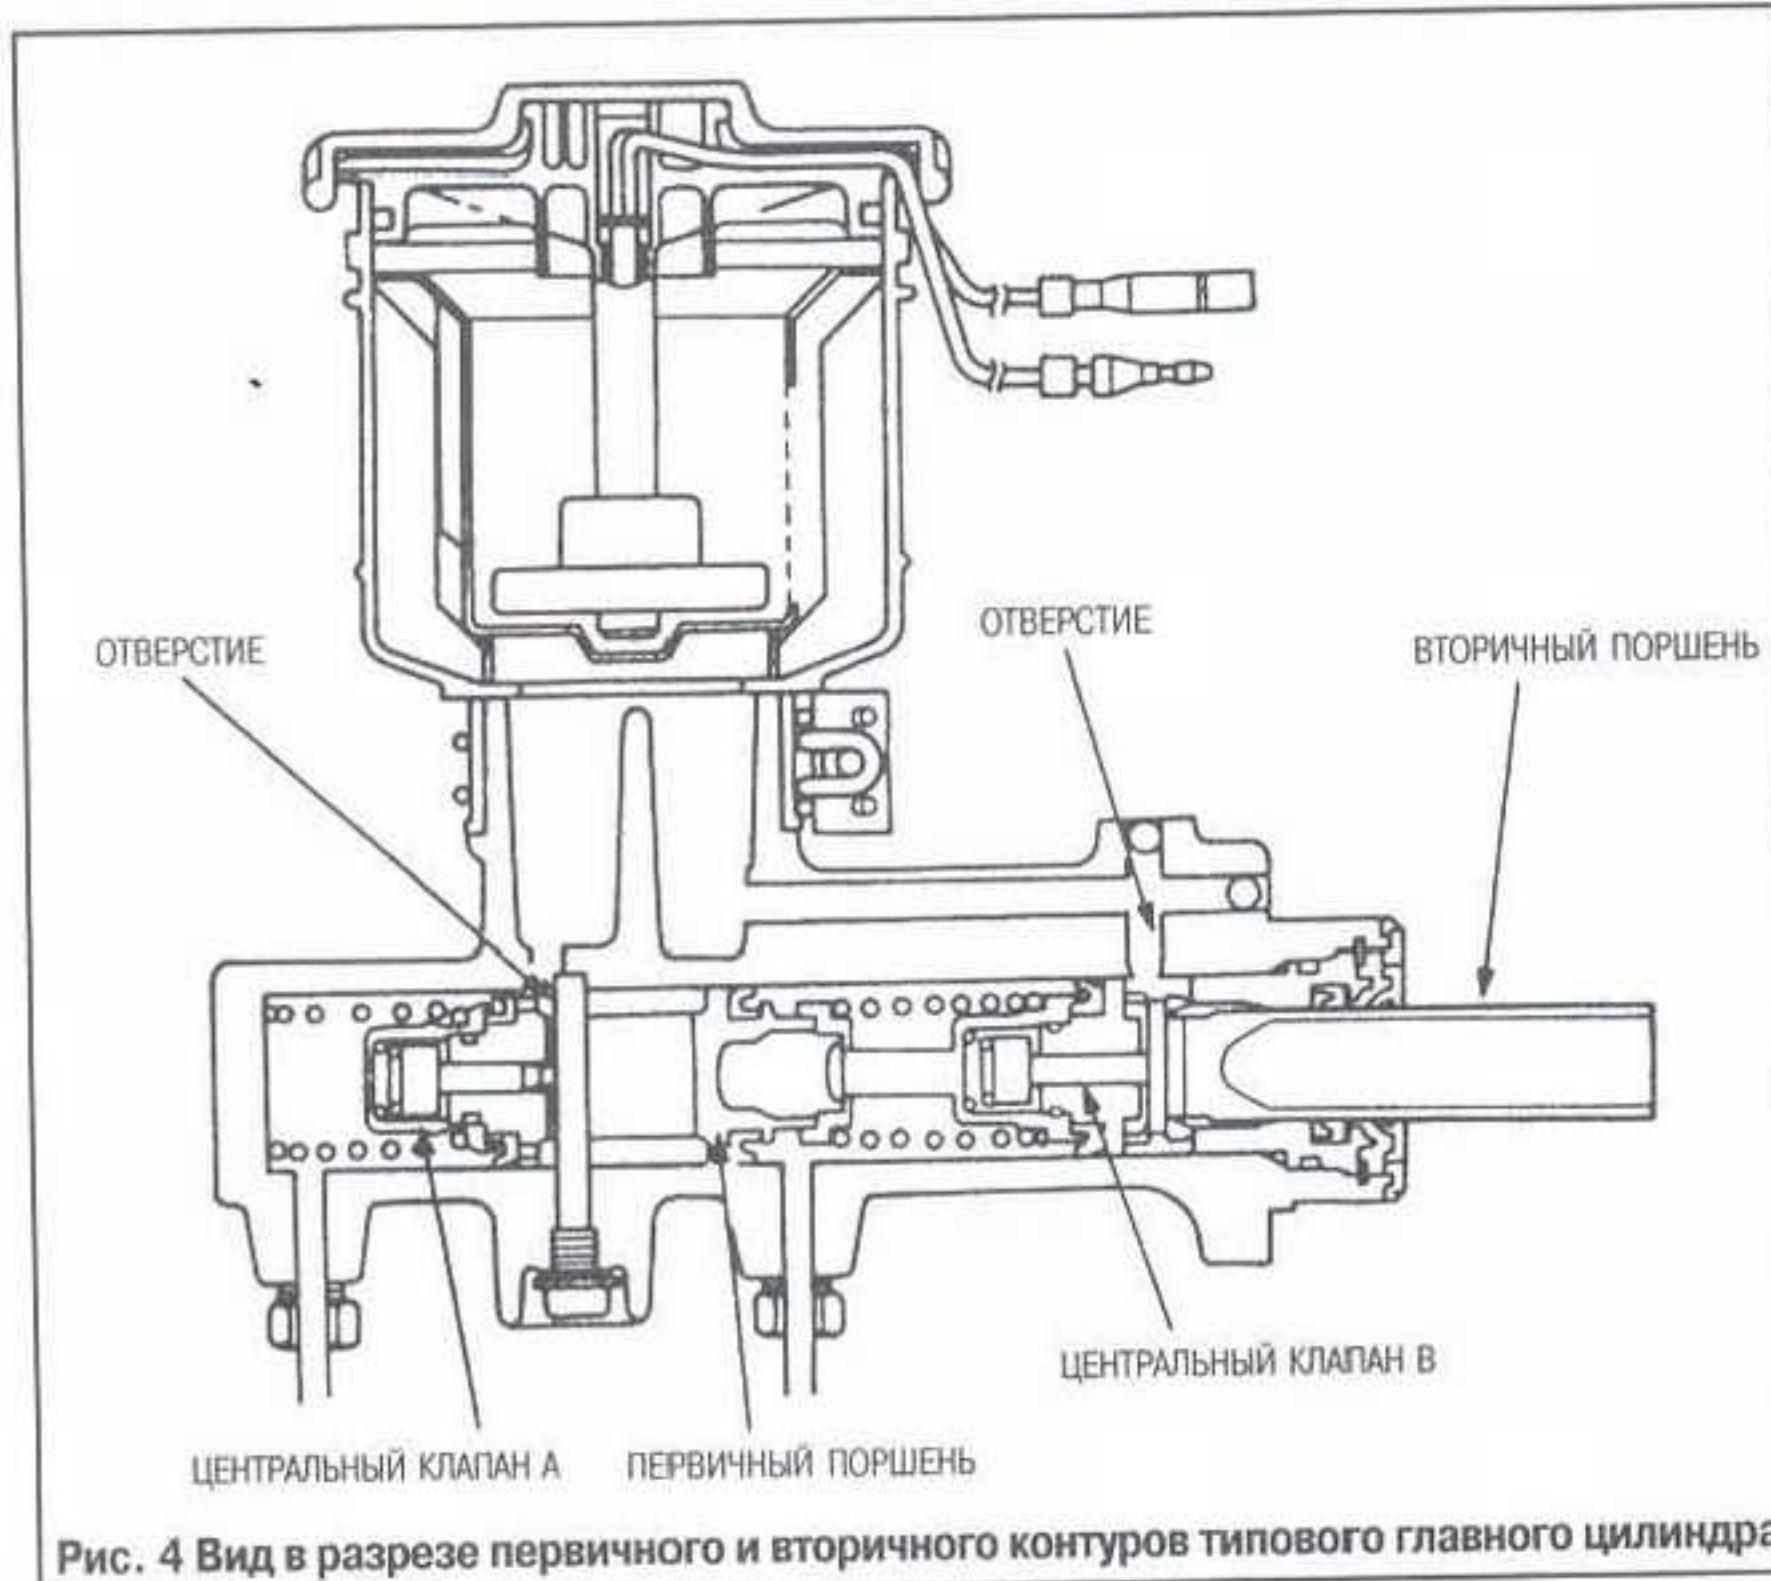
Вид в разрезе первичного и вторичного контуров типового главного цилиндра
